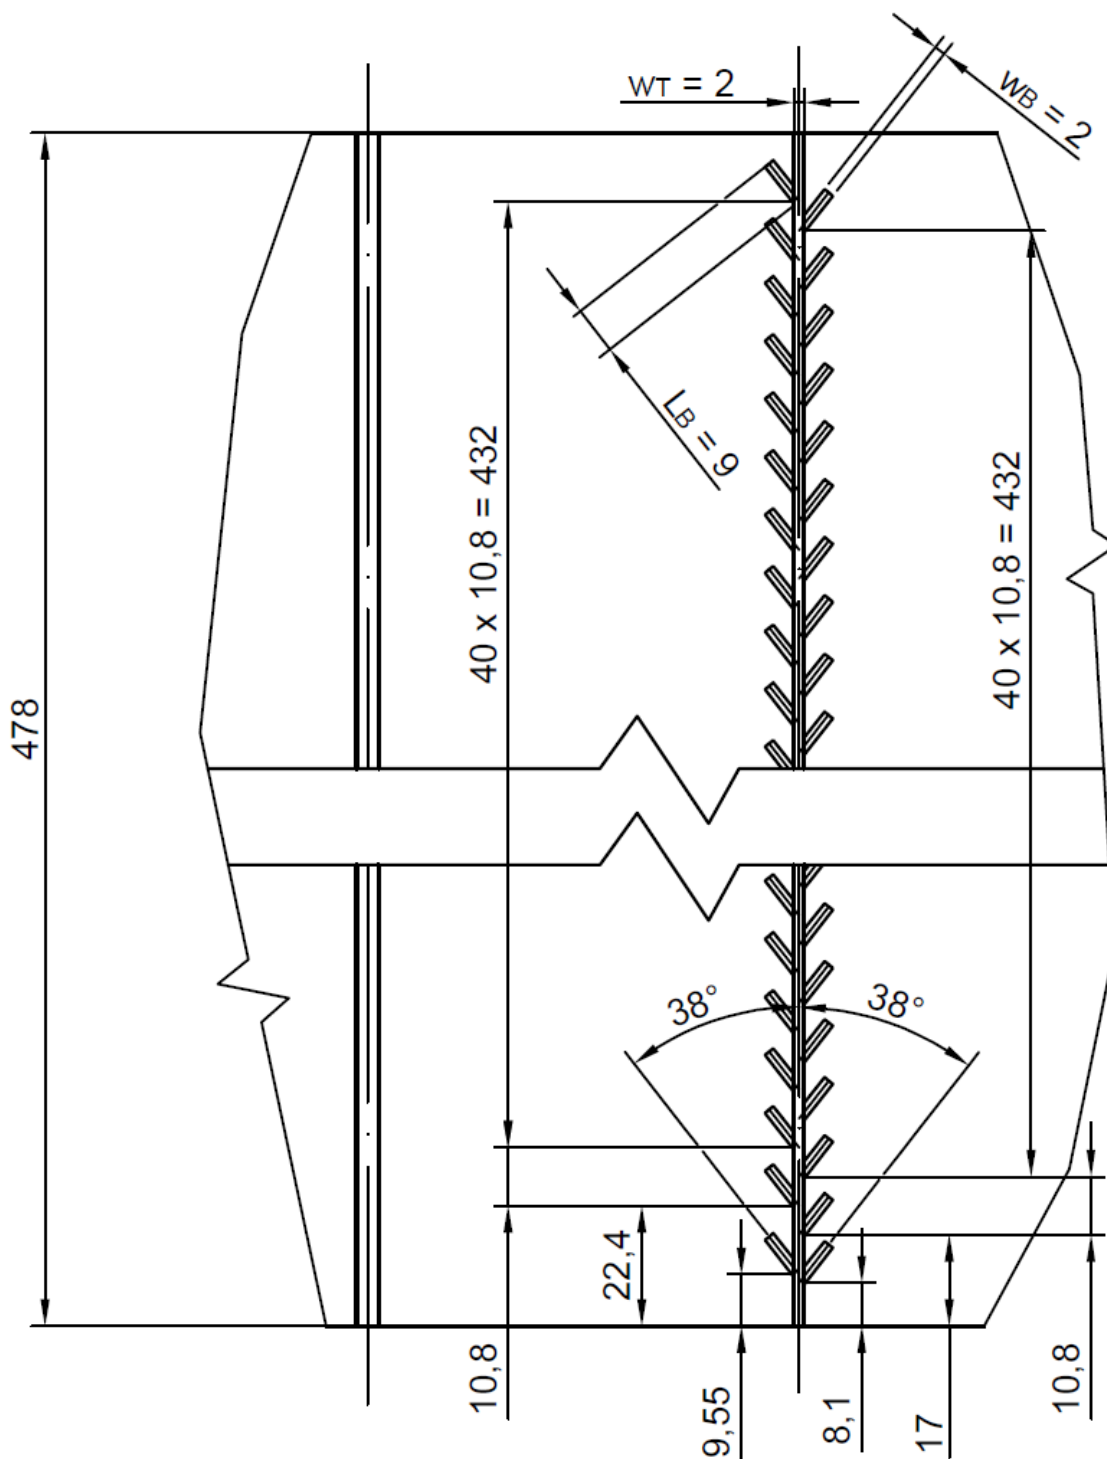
Výkres základního MKP modelu vyztuženého panelu
